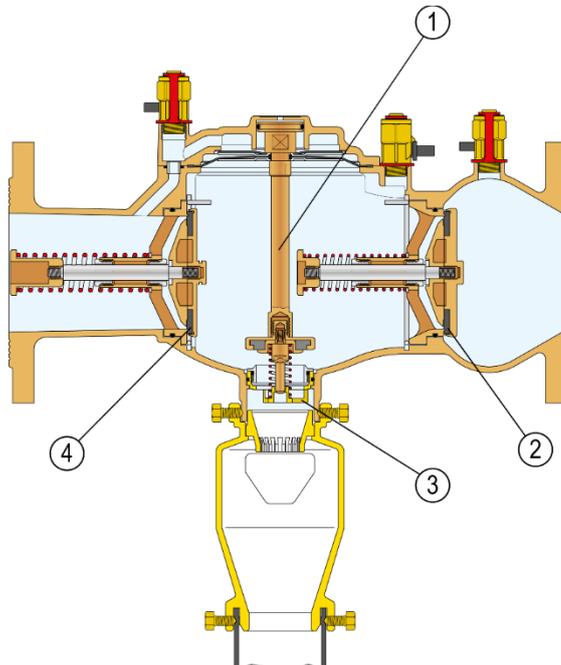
Parti soggette a usura disconnettore Euro GENO-DK 2 Maxi
